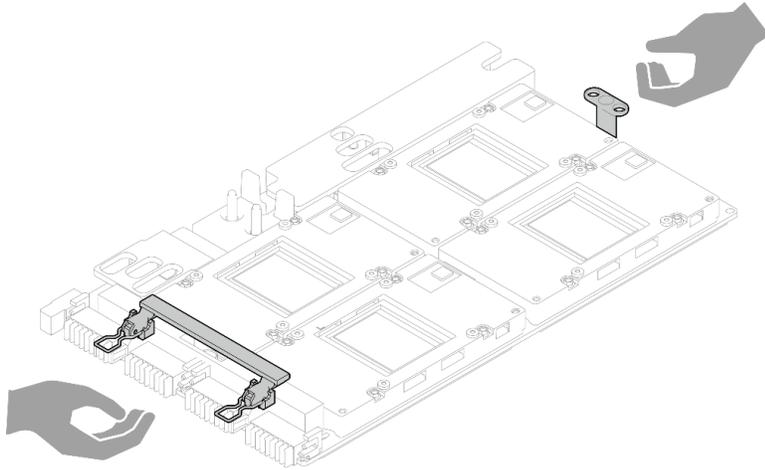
Extracción del conjunto de la placa de la GPU de la caja del paquete
